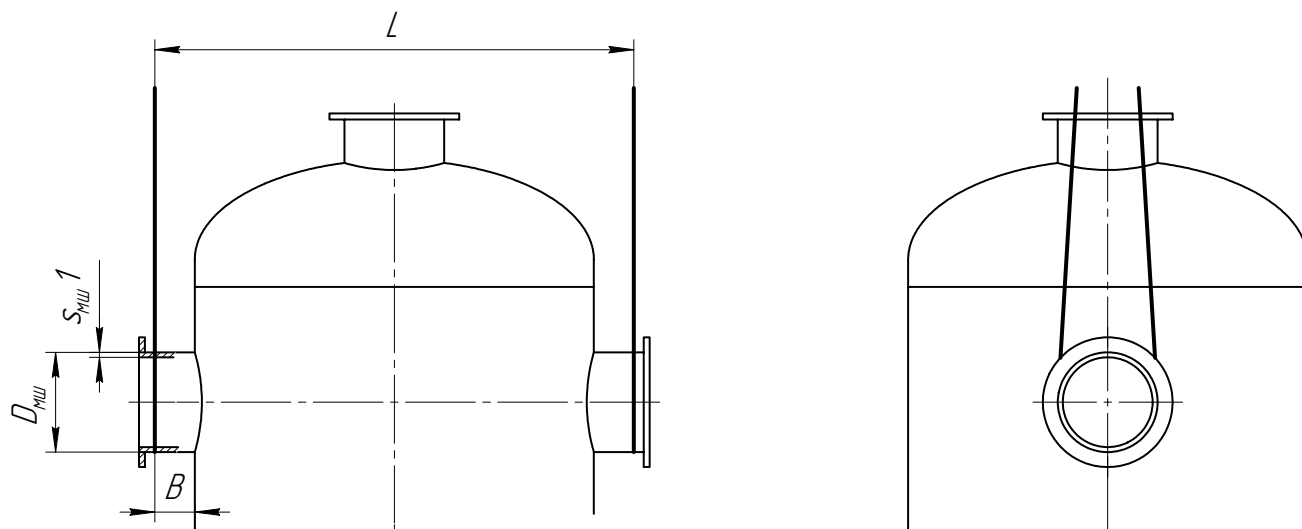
Схема к расчету стропов и монтажных штуцеров
